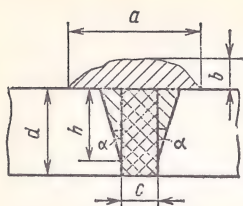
Эскиз поперечного сечения сварочного узла
